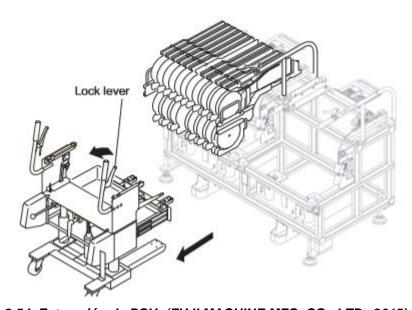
Extracción de PCU; (FUJI MACHINE MFG. CO., LTD., 2015)
